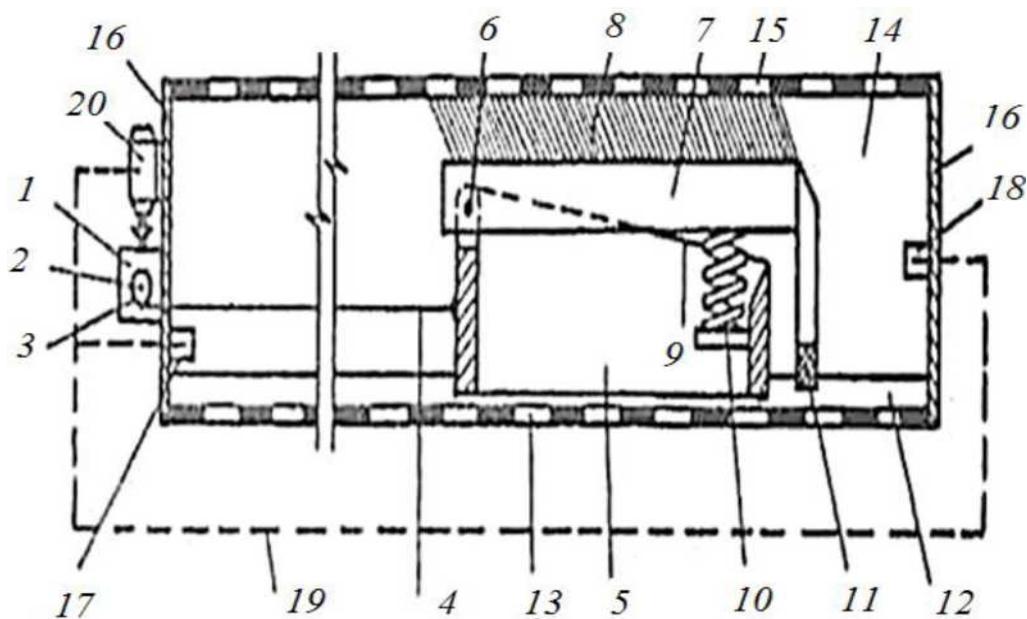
Очисник сита: 1 - редуктор; 2 - вал; 3 - шків; 4 - трос; 5 - колодка; 6 - шарнір; 7 - корпус щітки; 8 - ворс щітки; 9 - бічні стінки колодок; 10 - пружина; 11 - очисники; 12 - напрямні; 13 - Фордон; 14 - корпус сита; 15 - сито; 16 - бічні стінки корпусу сита; 17,18 - кінцеві вимикачі; 19 - електричний зв'язок; 20 - електродвигун
